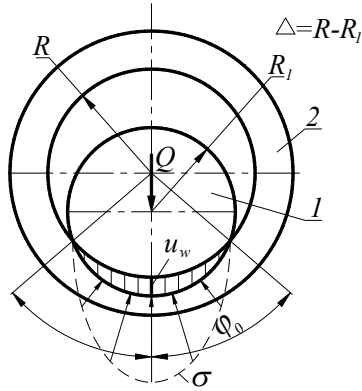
Розрахункова схема циліндричного підшипника ковзання
